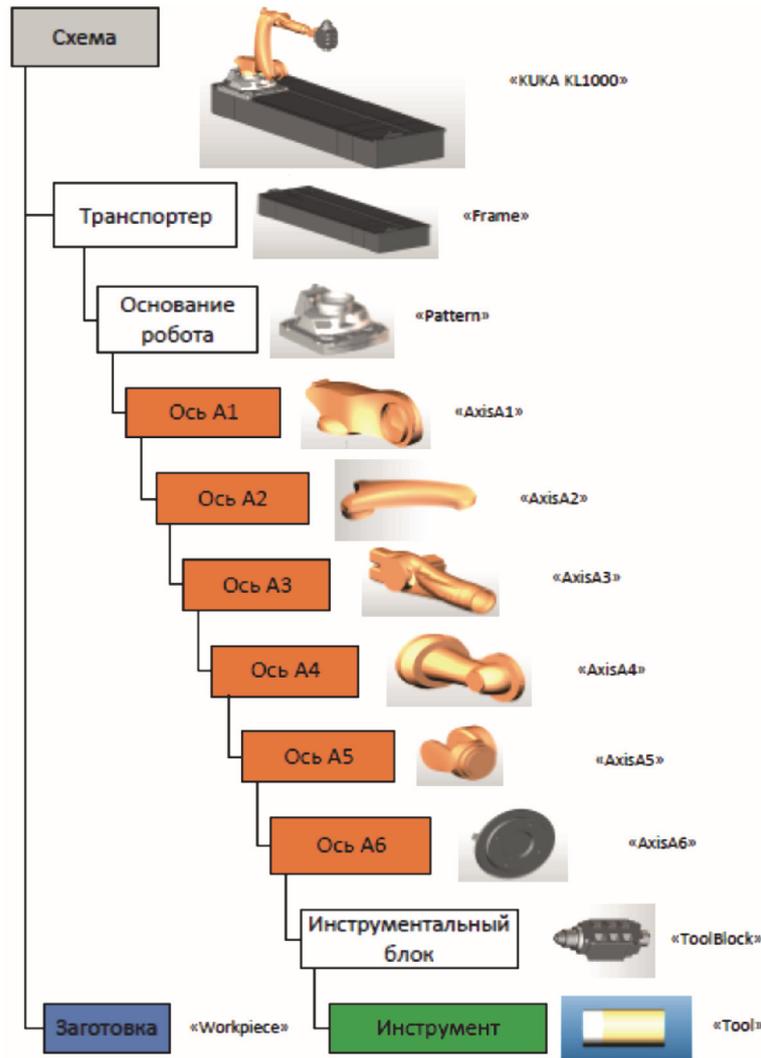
Представление трехмерной модели для построения кинематической схемы РТК обработки аэродинамического крыла
